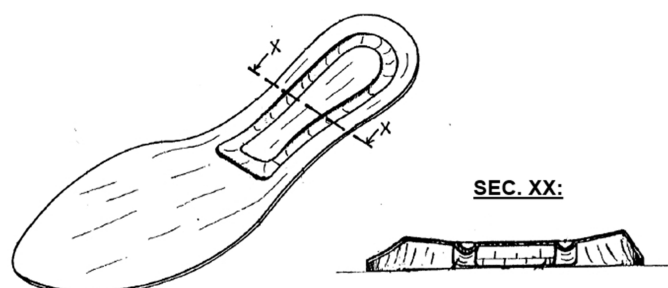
Inseto anti penetração proposta por Luigi Bettaglia, adaptado de [13]
